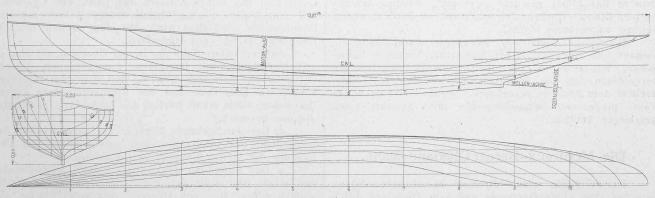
Motorboot «Fram». — Linienplan. Masstab 1:75.
